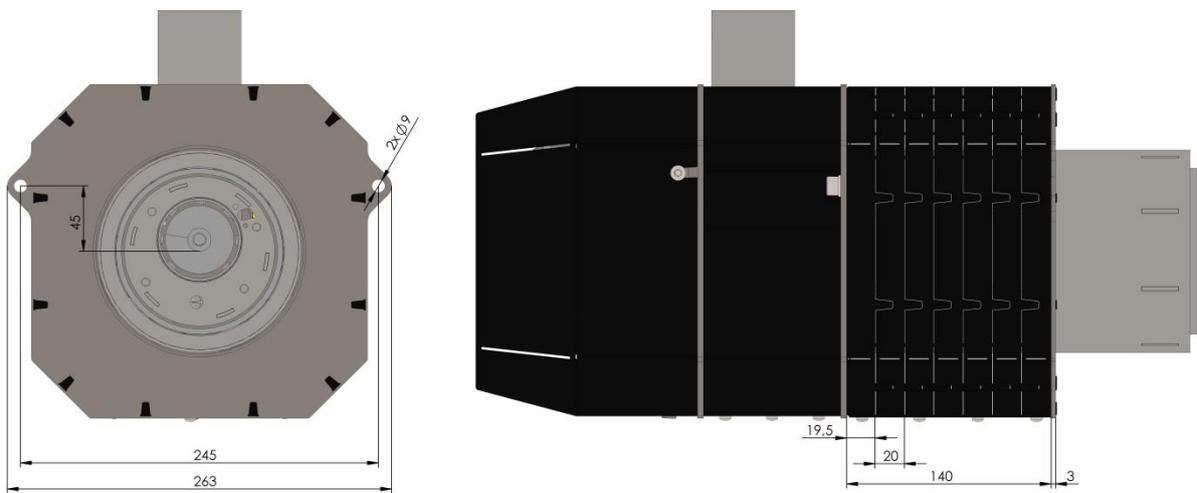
Ansicht des Brenners 8-36 kW mit einem Wärmedämmmantel und einer Montageplatte
